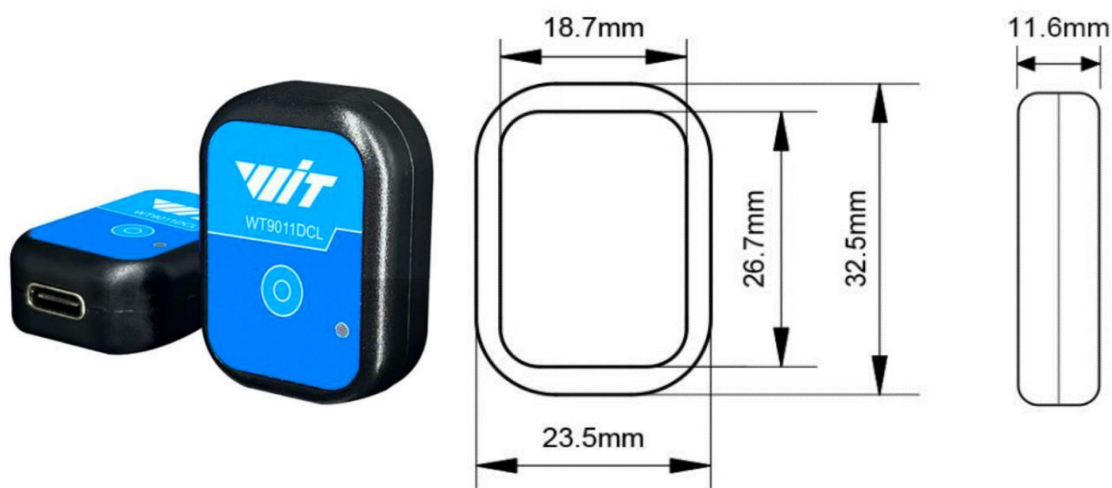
Внешний вид и габаритные размеры диагностического датчика ЦИКБД
